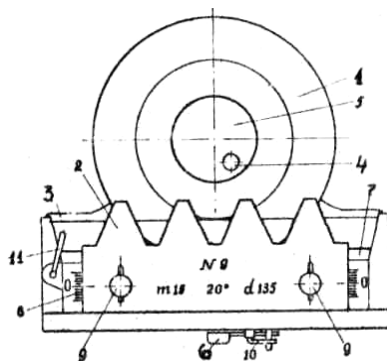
Принципиальная схема прибора ТММ-42 для нарезания зубчатых колес рейкой: 1 – диск для закрепления заготовки; 2 – инструментальная рейка; 3 – станина; 4, 5 – закрепляющие шайбы; 6 – рычаг храпового механизма; 7 – каретка; 8 – шкала; 9 – фиксаторы сдвига рейки; 10 – рычаг свободного хода рейки; 11 – рычаг свободного хода заготовки
